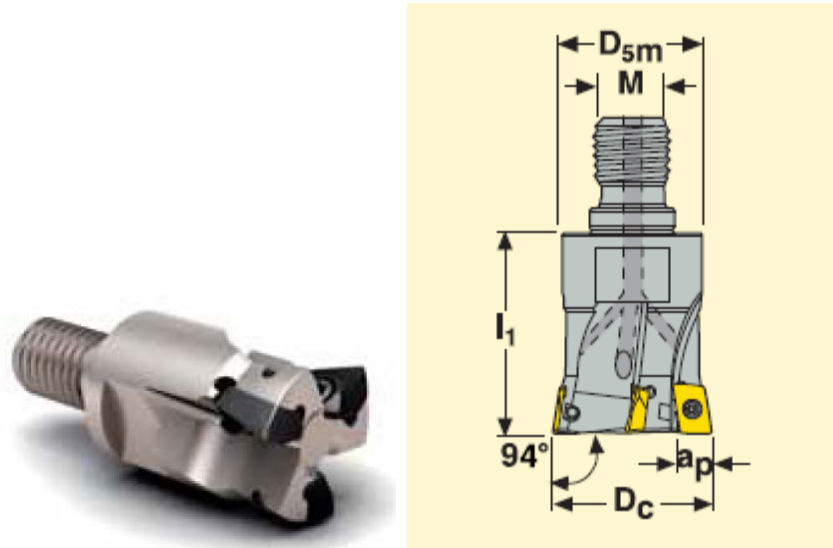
Фреза для врезного фрезерования R217.79–1638.RE-09-5AN
